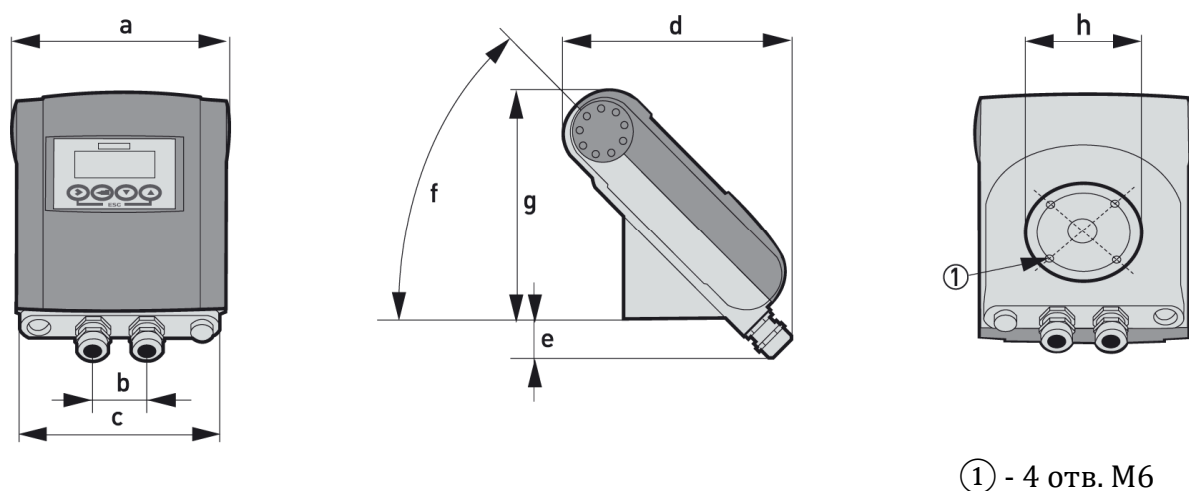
Габаритные размеры версии с наклоном 45°
